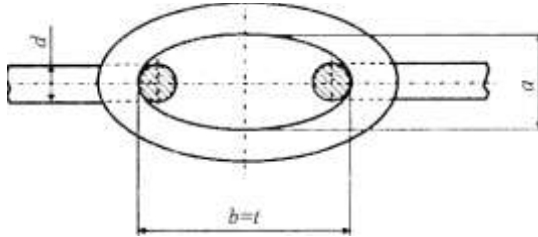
Конструкція ланки зварного ланцюга [4]
